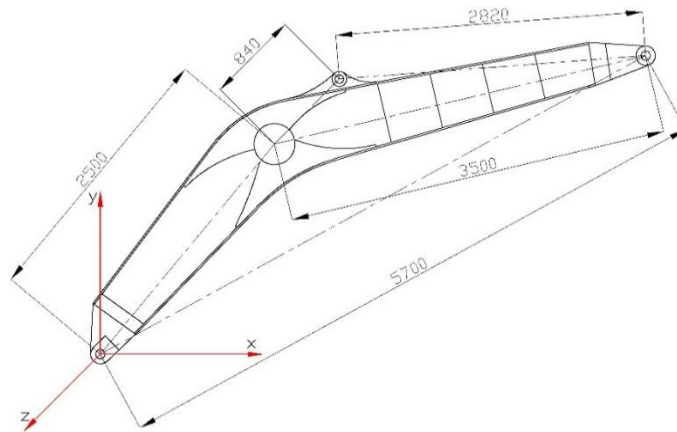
Pandangan Depan *Boom Excavator* Kelas 20 Ton *Reinforcement* Versi *Engineer PT. PQR
